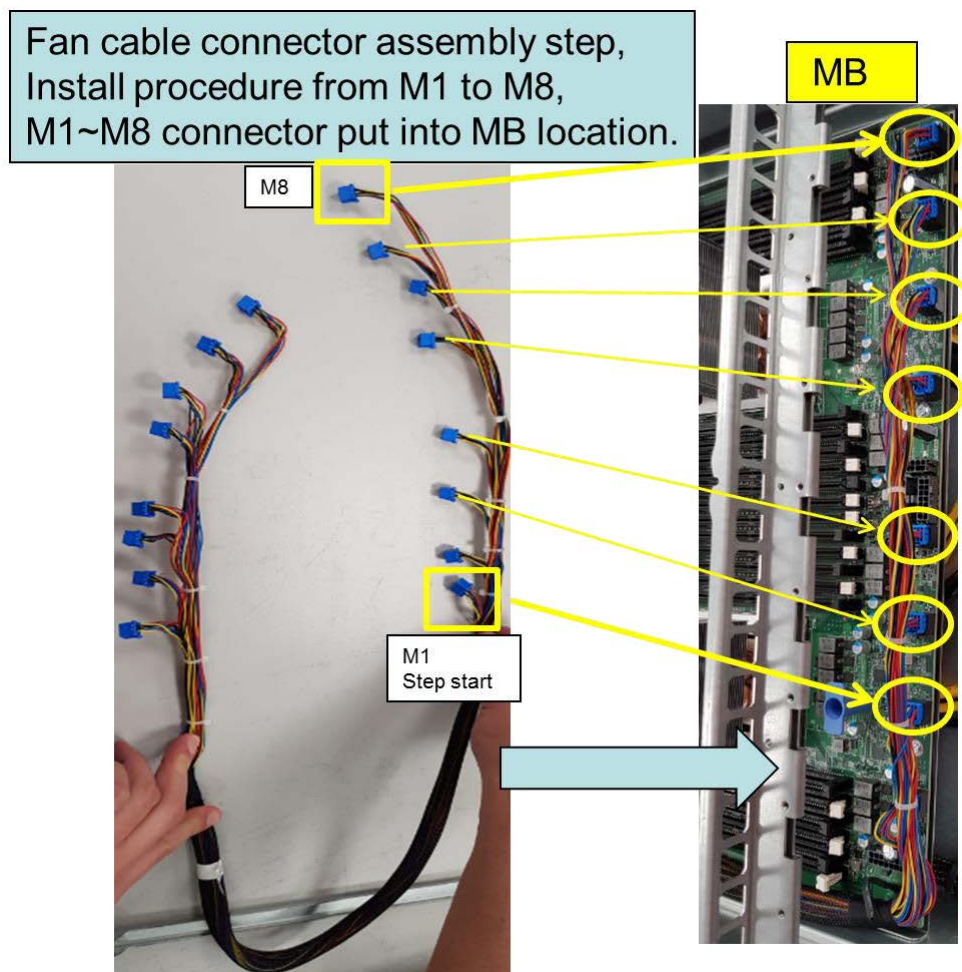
Assemblage du câble de ventilateur MB-PDB vers MB
